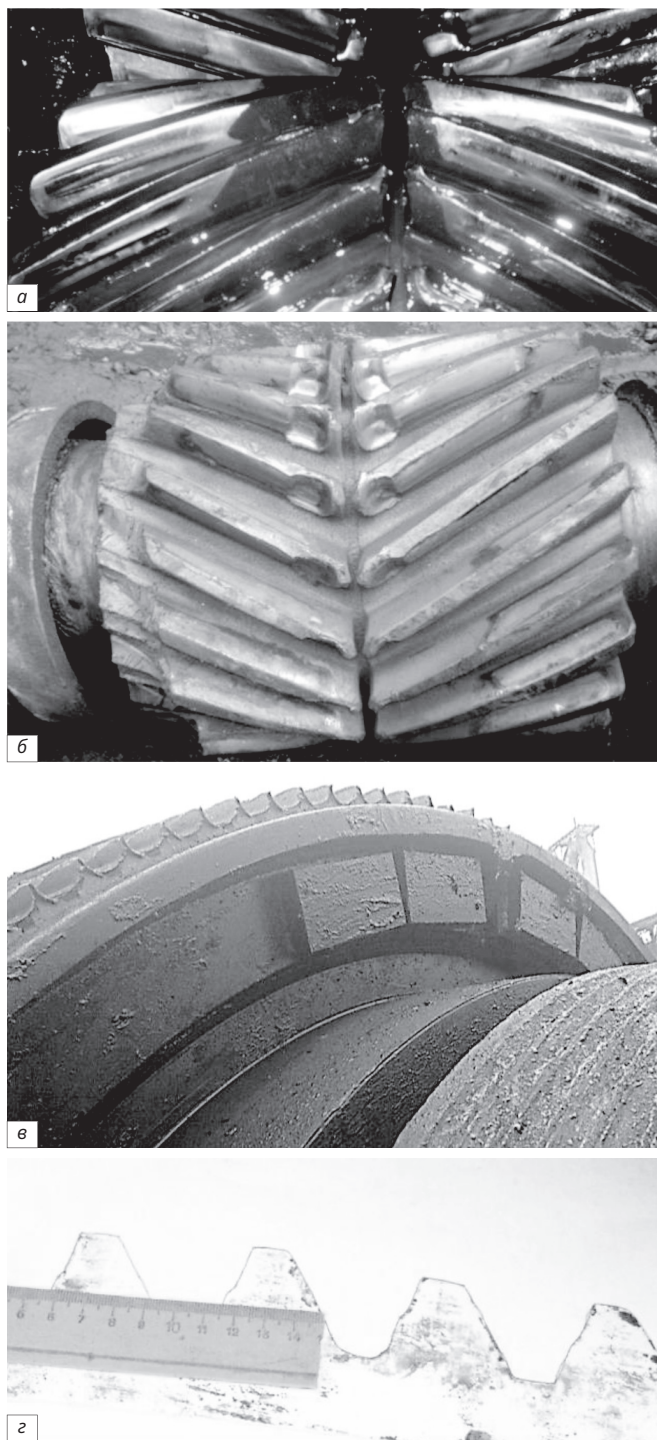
Повреждения зубчатых передач скиповой лебедки: а — смещение пятна контакта; б — разрушение зубьев; в — промежуточный вал; г — износ венца барабана
